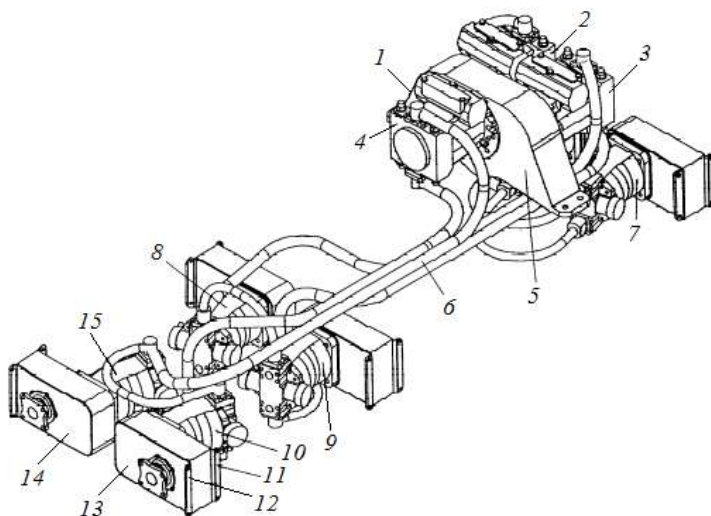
Компонівка елементiв конструкцiї ГОТ: 1 – насосна станцiя; 2, 3, 4 – гiдравлiчнi насоси; 5 – узгоджуючий редуктор; 6 – трубопроводи; 7, 8, 9, 10, 15, 16 – гiдравлiчнi мотори; 11, 12 – фланцi; 13, 14 – коробки
